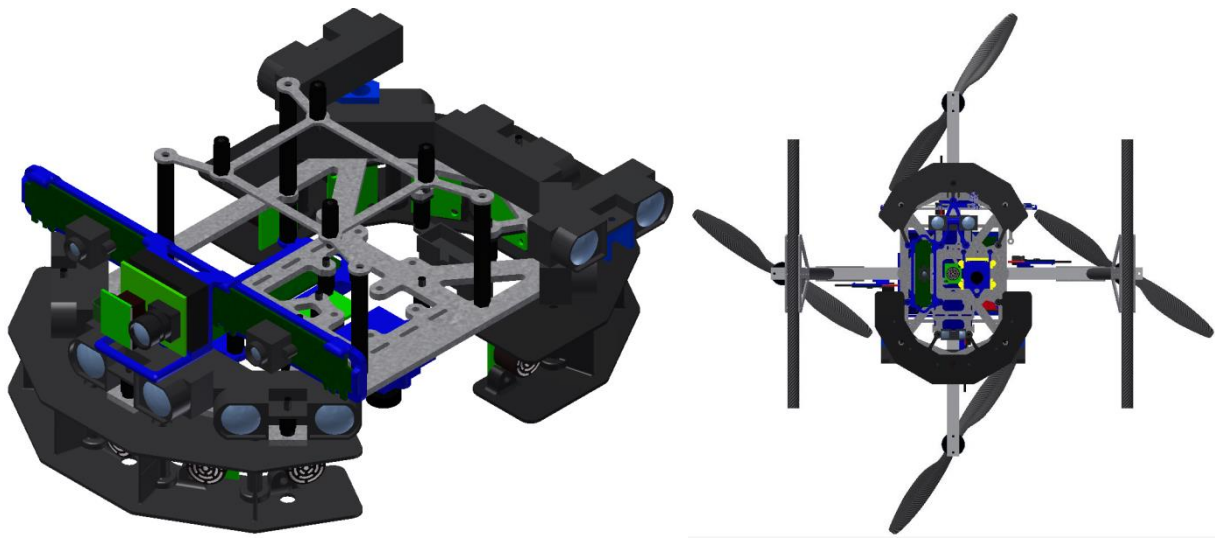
Ebenen 5-7 (links) und Bodenansicht auf Bodenplatte (rechts) des AQopterI8, CAD Design (CAD Zeichnung Sascha Dechend)
